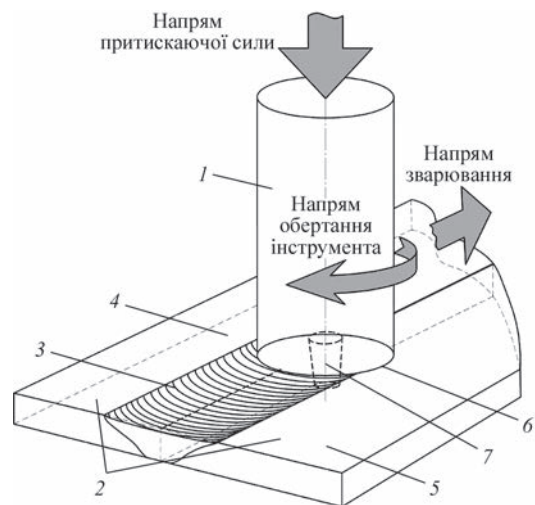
Процес зварювання двох пластин [1]: 1 — інструмент; 2 — пластини; 3 — зварний шов; 4 — сторона набігу інструмента; 5 — сторона повернення інструмента; 6 — заплечик; 7 — штир
